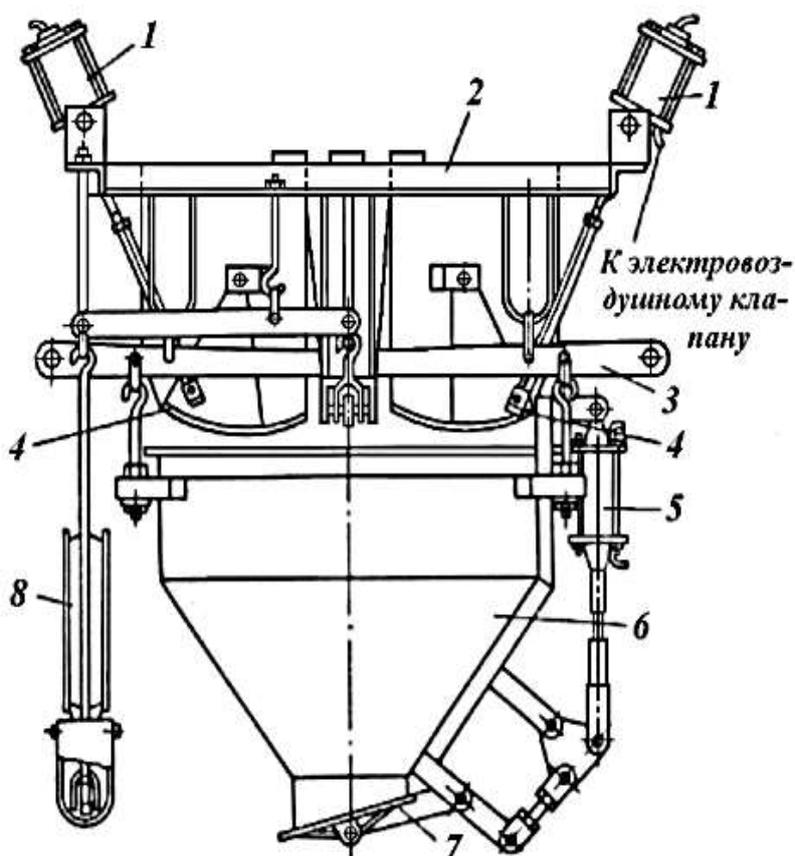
Автоматический весовой дозатор: 1 – пневмоцилиндр впускного затвора; 2 – рама; 3 – весовая рычажная система; 4 – секторный затвор; 5 – пневмоцилиндр выпускного затвора; 6 – весовой бункер; 7 – выпускной затвор; 8 – циферблатный указатель
